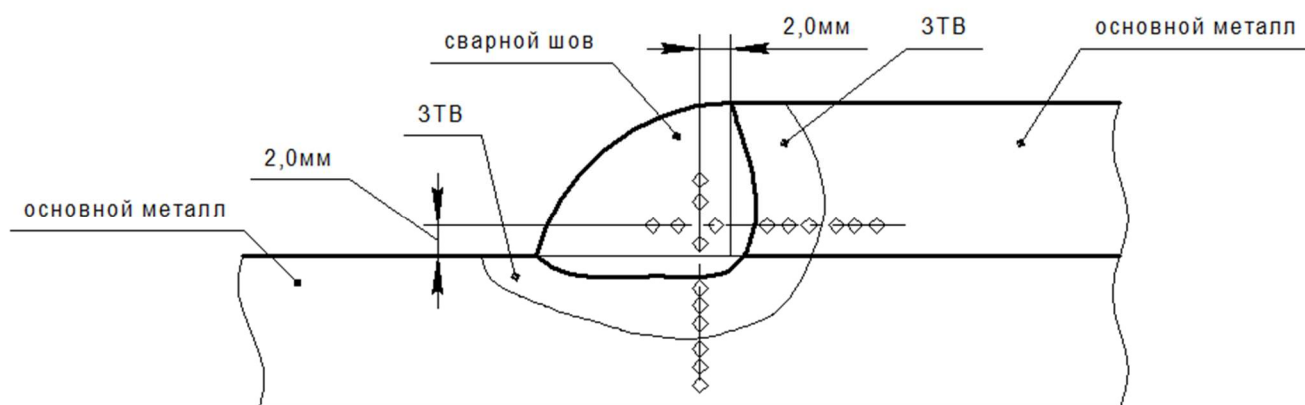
Схема измерения твердости (HV_{10}) в различных зонах нахлесточного сварного соединения
